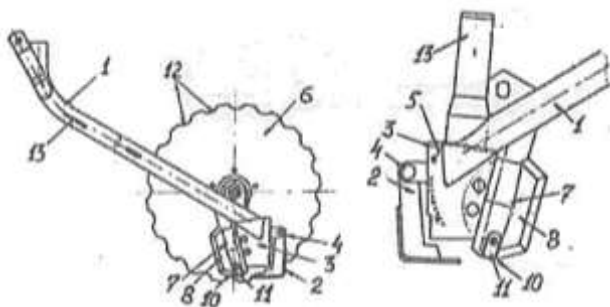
Однодисковый сошник с вырезным диском: 1 – семяпровод; 2 – клапан; 3 – корпус; 4 – шарнирное соединение; 5 – отражатель; 6 – диск; 7 – нож; 8 – передняя кромка ножа трапецеидальной формы; 10 – рабочая кромка ножа; 11 – защитная пластина на рабочей кромке ножа; 12 – выемки радиальной формы; 13 – труба-воздуховод
